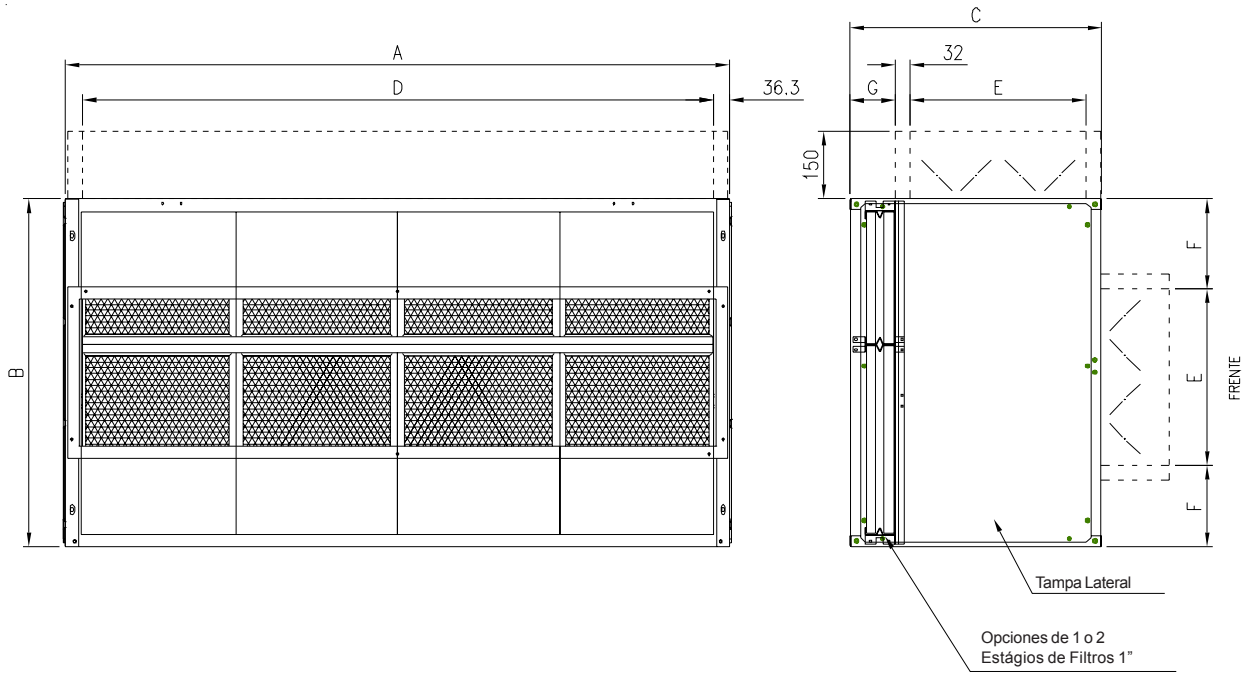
Dimensional Módulo Serpentin 350 a 500
